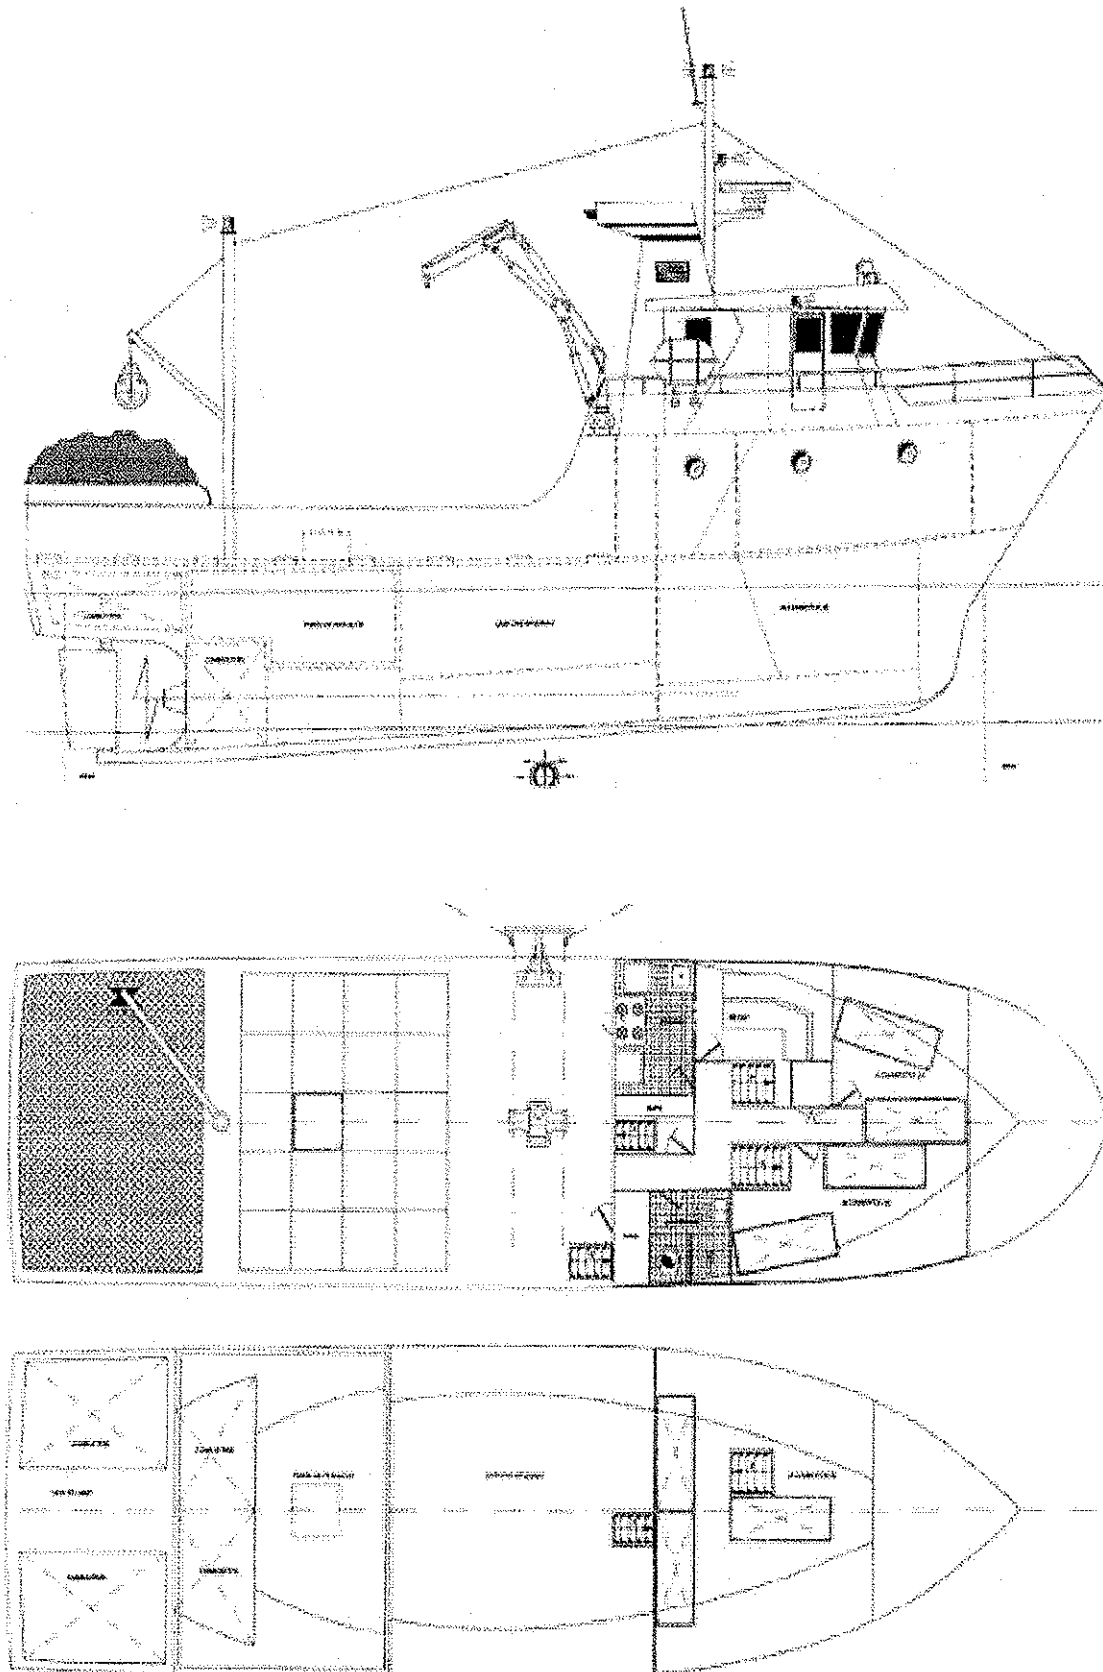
Embarcação protótipo da “Nautiber” –Perfil e cortes longitudinais.
